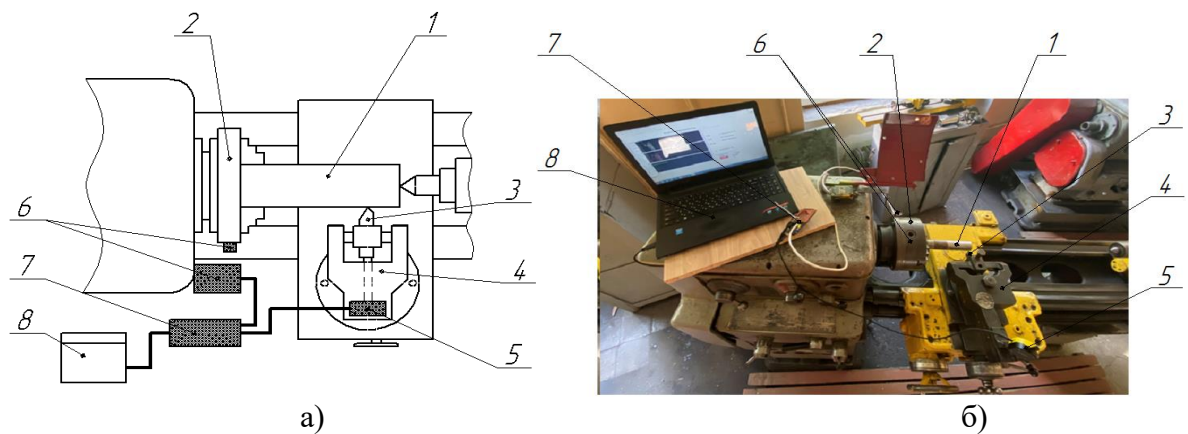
Стенд для дослідження сили різання на токарно-гвинторізному верстаті: а – схема стенда; б – загальний вигляд стенда; 1 – заготовка для токарного обробітку; 2 – трьохкулачковий самоцентруючий патрон; 3 – токарний різець; 4 – динамометр кручення ДК1; 5 – індикатор з цифровим відліковим пристроєм; 6 – давач обертів; 7 – плата Arduino Mega 2560; 8 – ПК.
